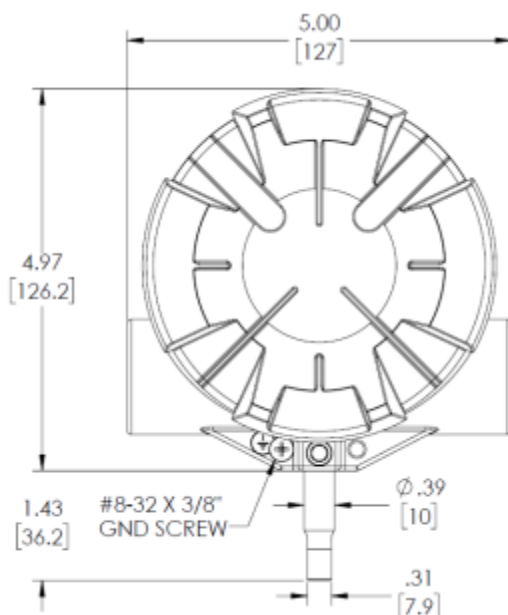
FL500 Umrisszeichnung, Frontansicht
